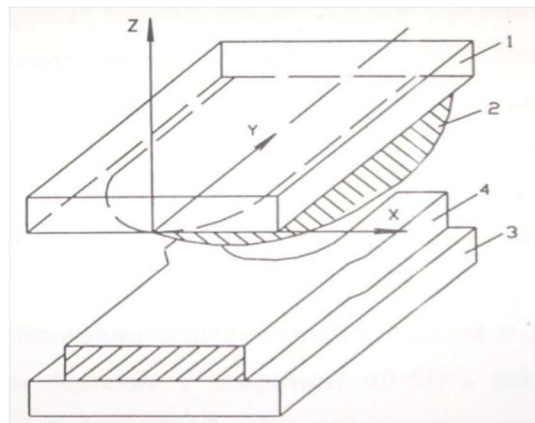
Ковка полосы эллипсоидным бойком [14]: 1 и 3 – верхняя и нижняя плоские плиты; 2 – эллипсоидный боек; 4 – заготовка
